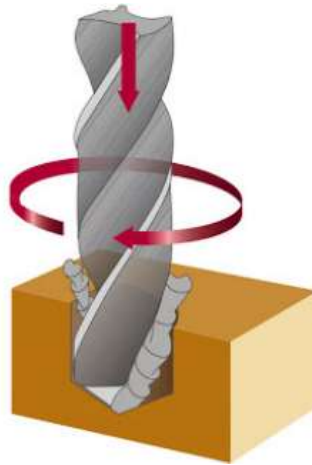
Movimientos de la broca y arranque de material [23]
